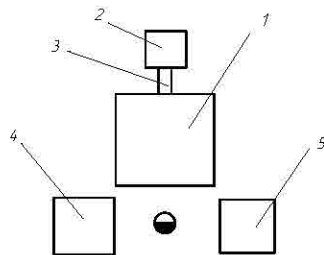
Організація робочого місця штампувальника для обрізання облою: 1- обрізний прес; 2-тара для поковок; 3-склиз; 4-тара для заготовок, 5- тара для облою.
